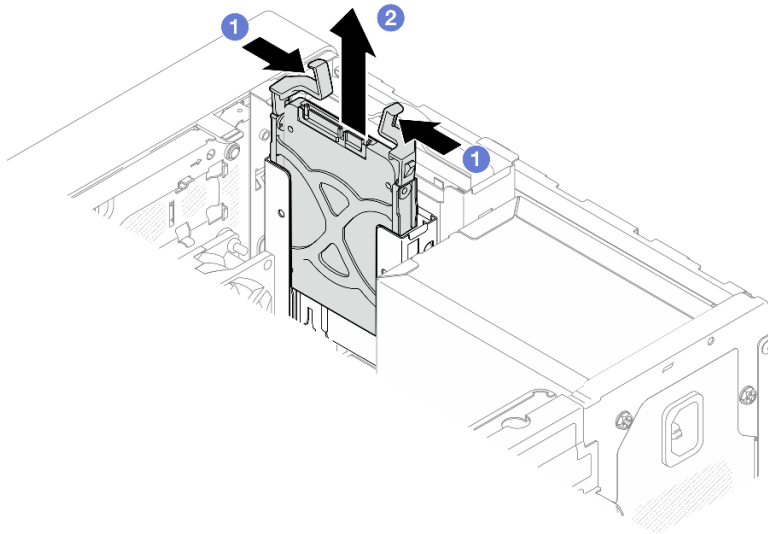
Entfernen einer Laufwerkbaugruppe aus Laufwerkposition 1
